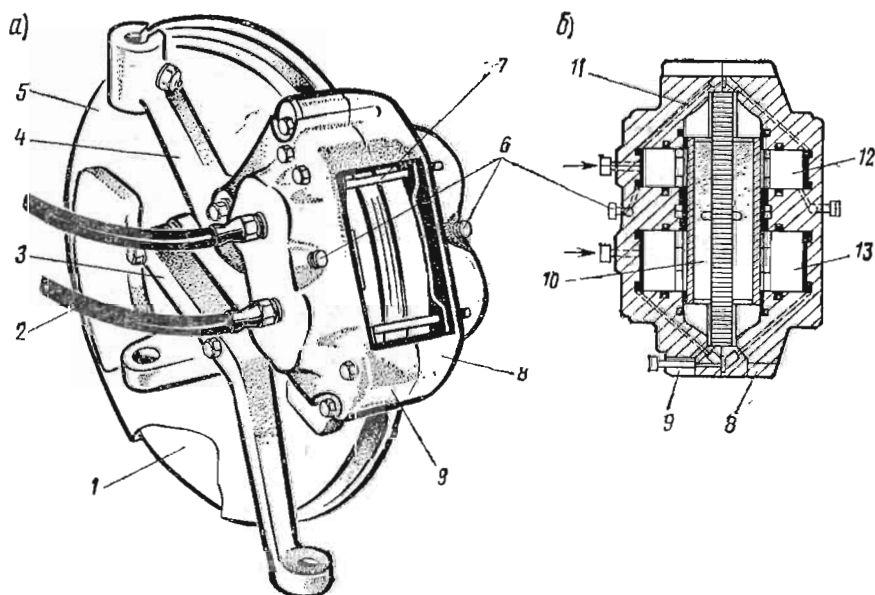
Дисковый тормозной колесный механизм автомобиля «Москвич-2140»:
